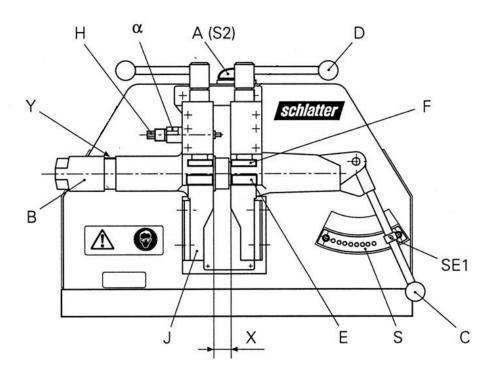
Máquina de soldar a topo tipo M , tabela de ajuste
